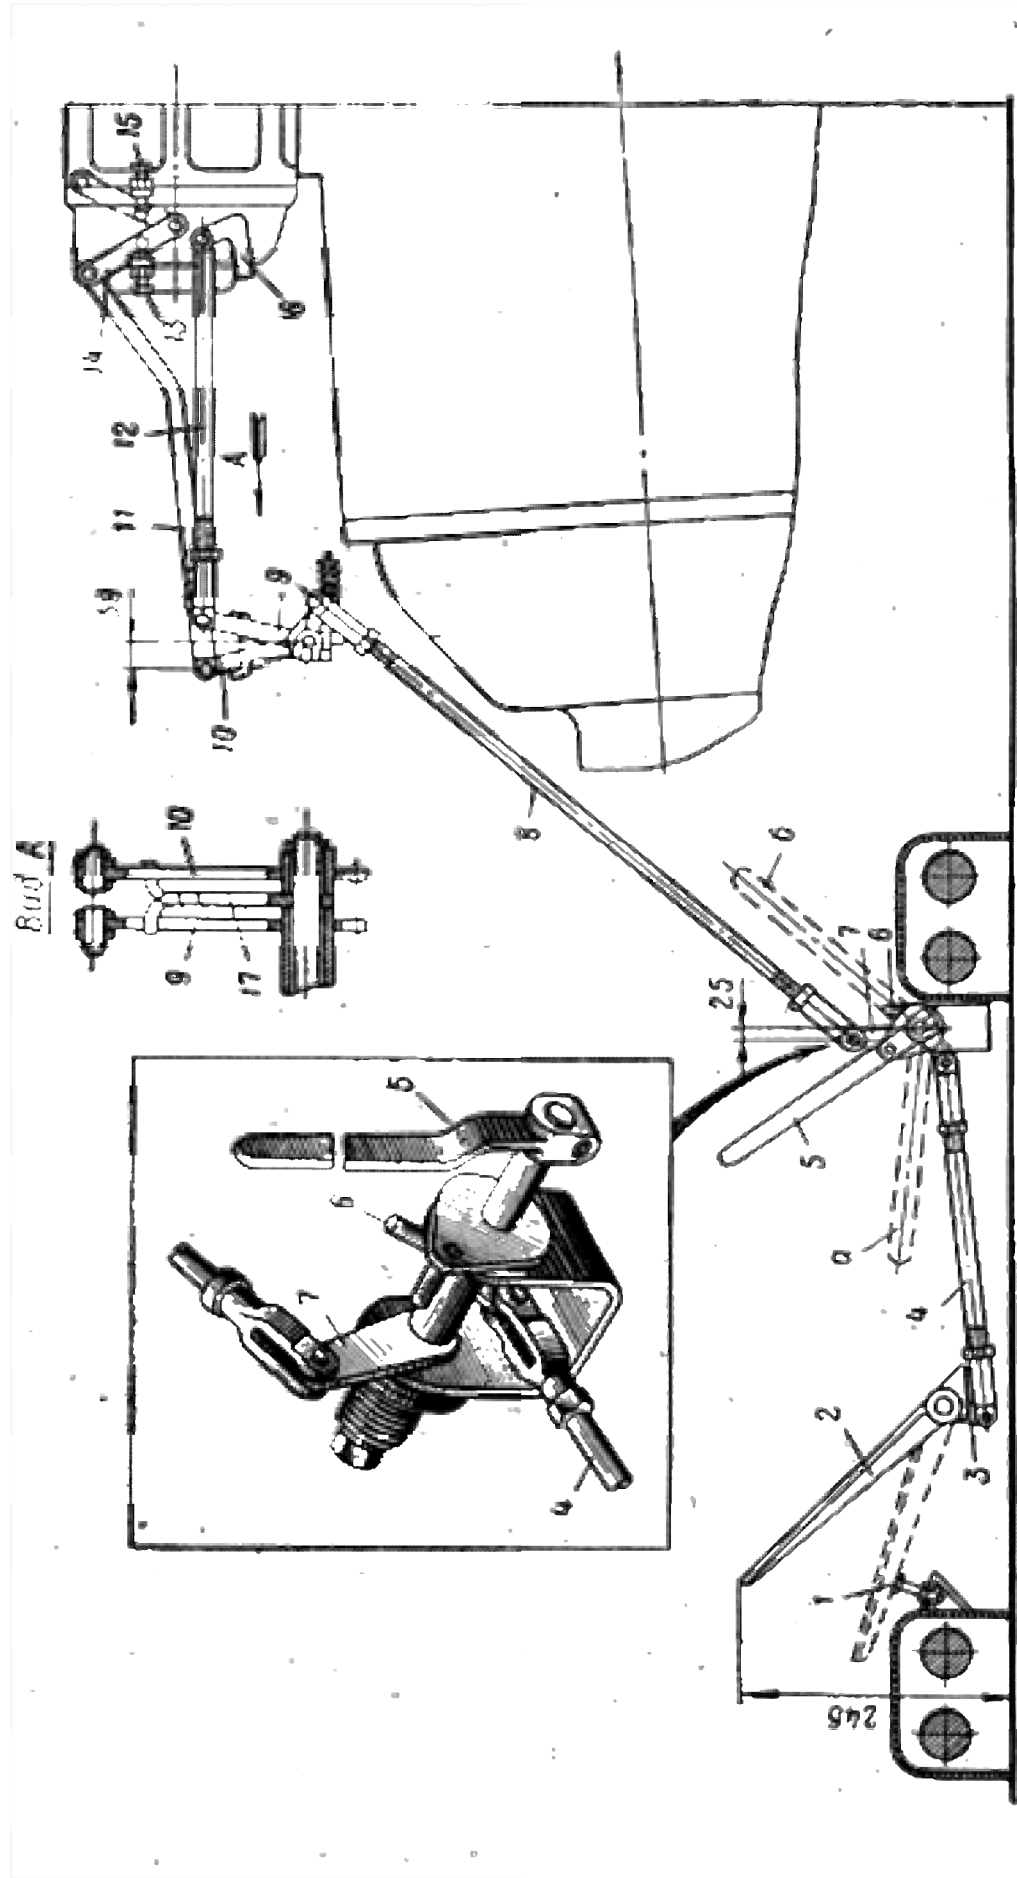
Схема регулировки привода управления двигателям транспортера-тягача МТ-ЛБ:
